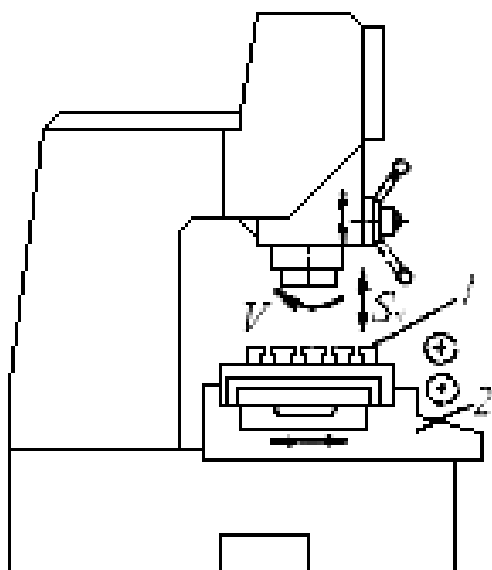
Загальний вигляд координатно-розточувального верстата з одним стояком
